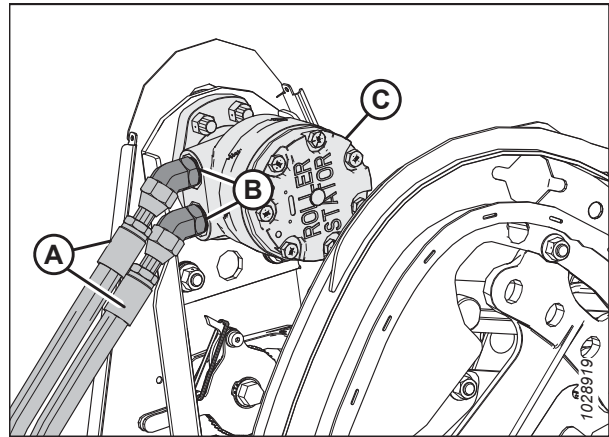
Haspelmotor und Hydraulikschläuche
